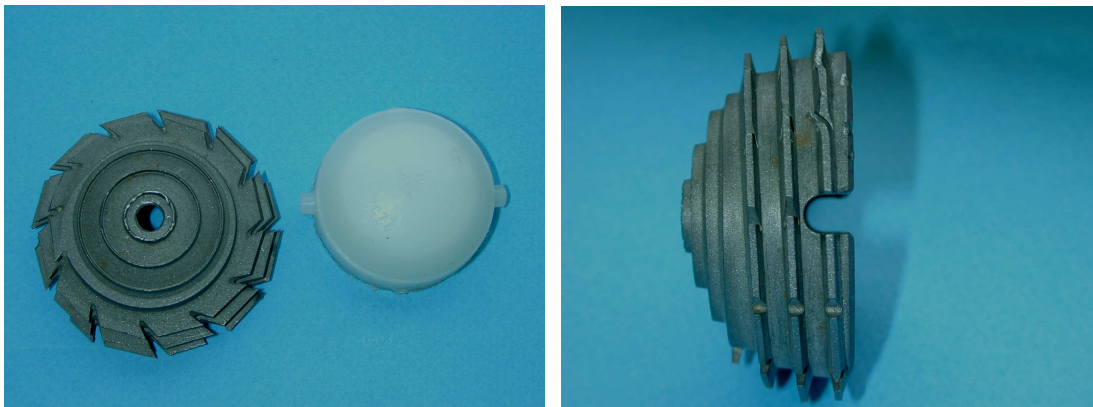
Schraubpfanne Lamella in der Aufsicht und der Seitenansicht.
